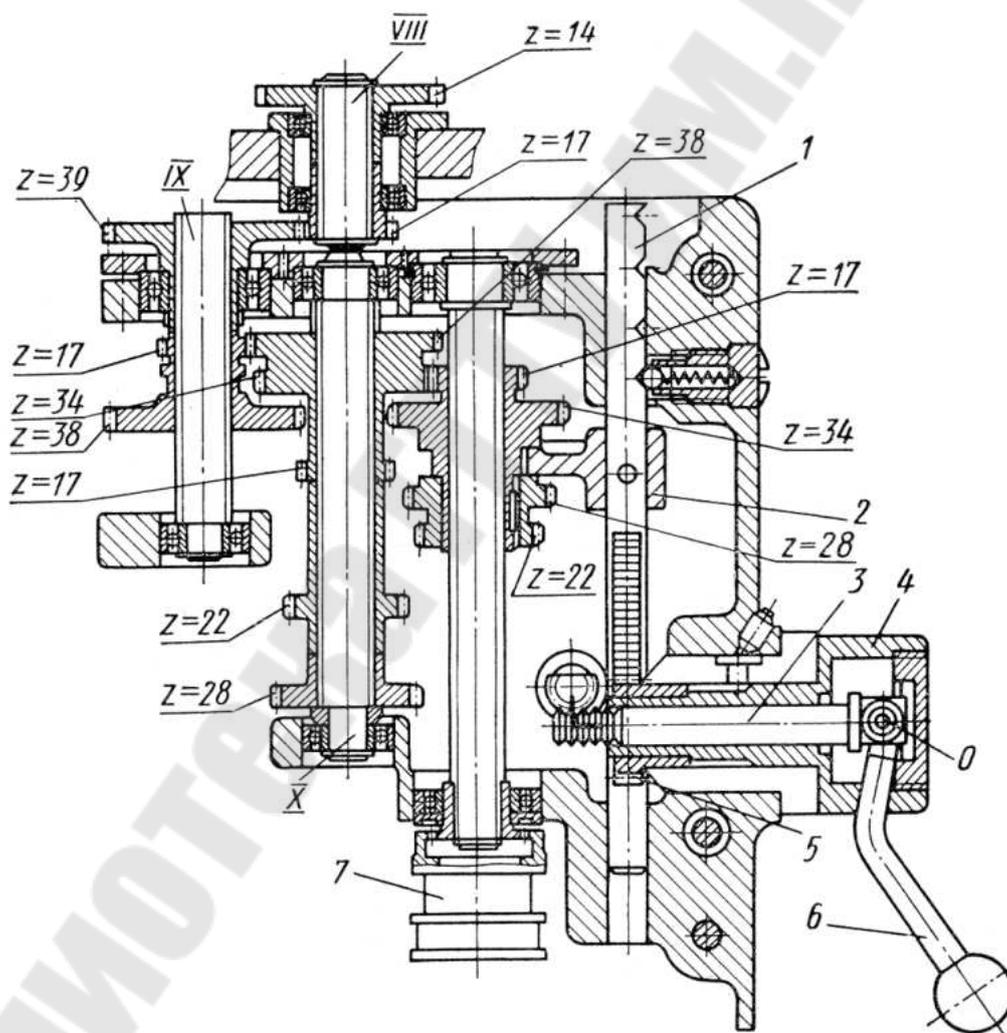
Коробка подачи сверлильного станка 2А53:
